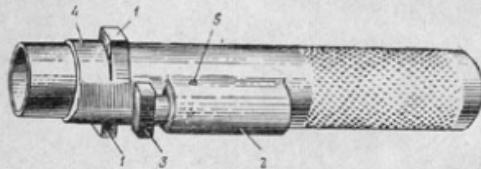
Направляющая трубка возвратно-боевой пружины:
